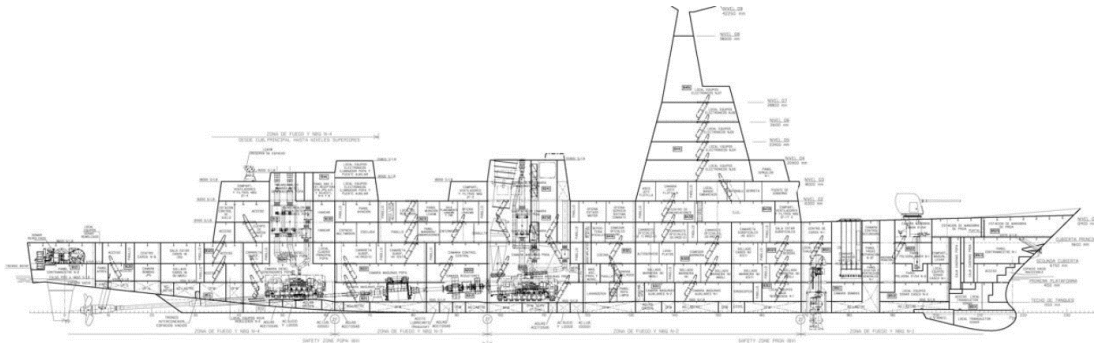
División en cubiertas y cuadernas de un buque [6]
